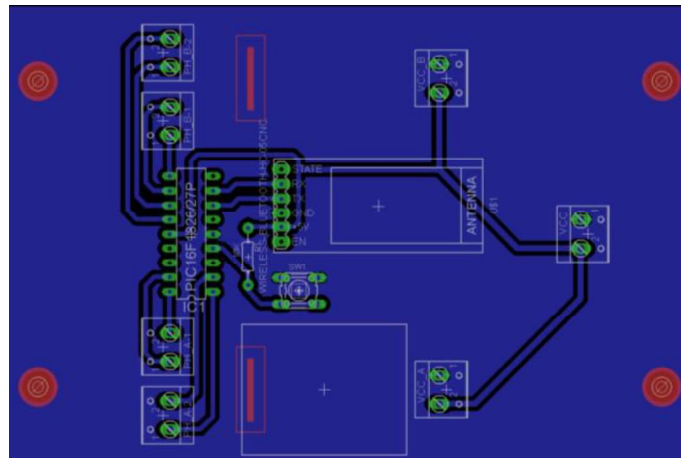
Diseño PCB de la tarjeta de control del mini robot.
